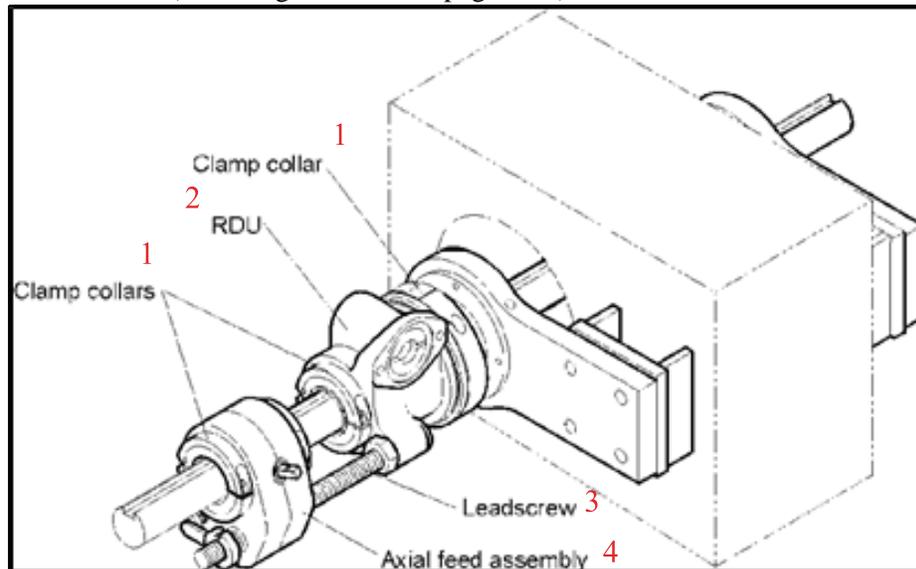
COMPONENTES DE DESMONTAJE AFU
